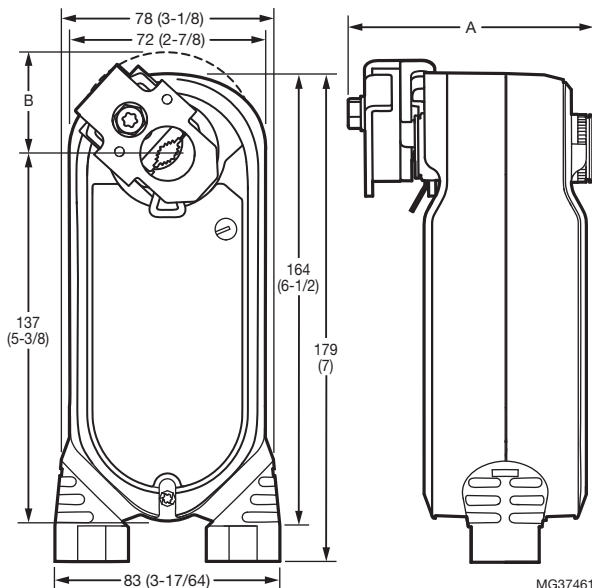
Plan dimensionnel de l'actionneur en mm (po). Voir le Tableau 2 pour les dimensions A et B.
